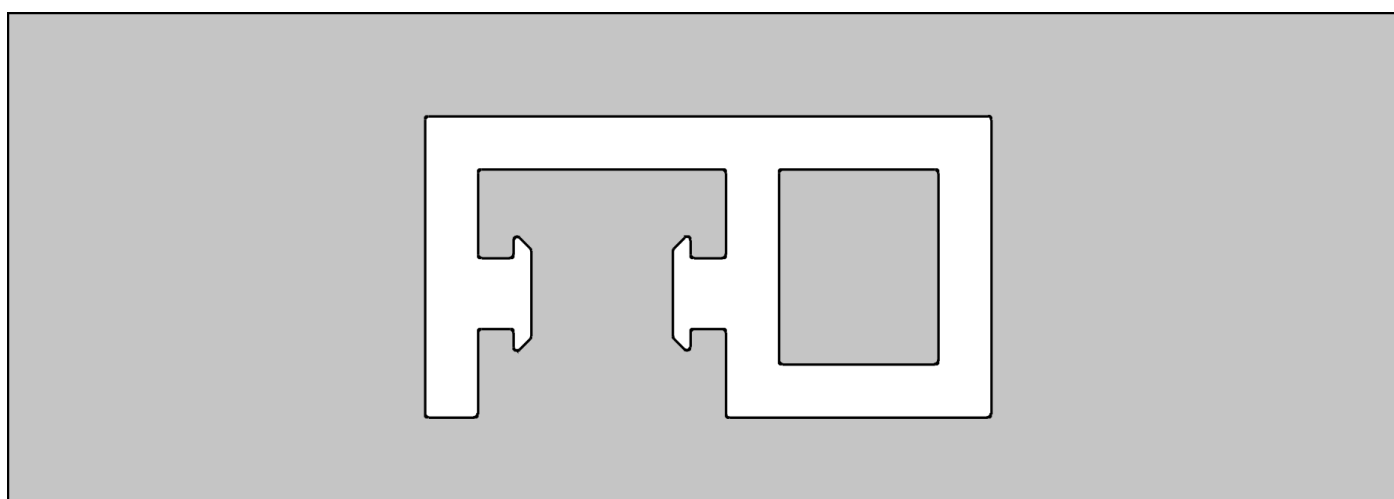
boquilla de extrusión pieza "12.1.- Tubo cableado"
